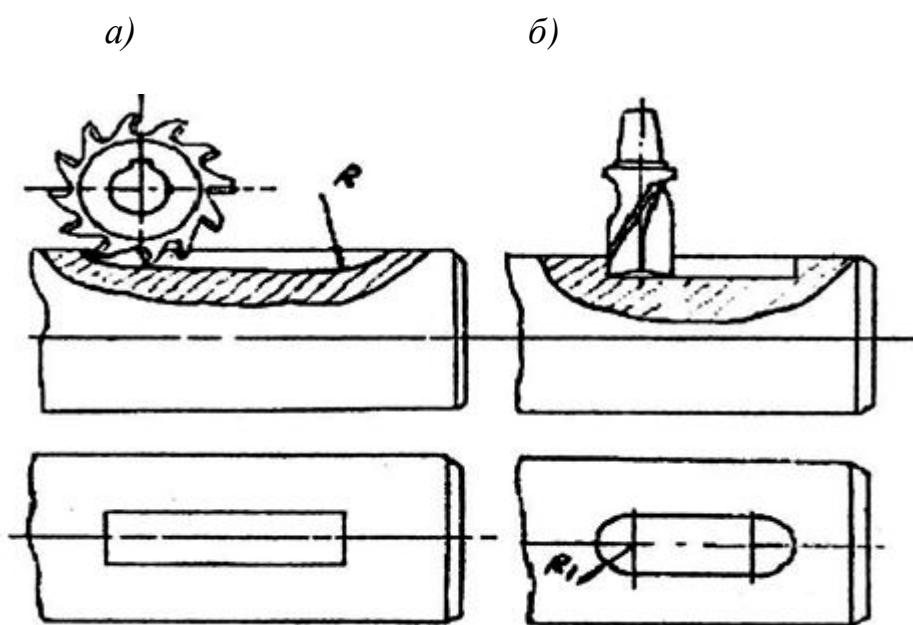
Изготовление шпоночной канавки дисковой (а)
